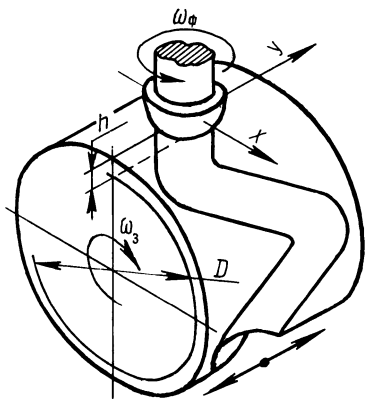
Схема фрезерования радиусной синусоидальной канавки на поверхности цилиндра
